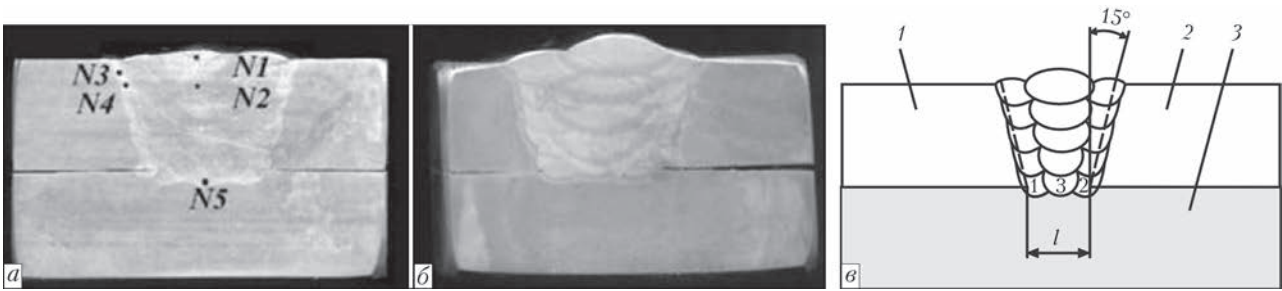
Налесточно-стыковое сварное соединение: а, б — макрошлиф соединения с использованием соответственно проволоки Св-08Г2С и ППс-ТМВ7; в — схема разделки кромок и сварки (1, 2 — стенка усиливающего элемента: муфты (1) и технологического кольца (2); 3 — стенка газопровода; l — зазор между элементами муфты)
